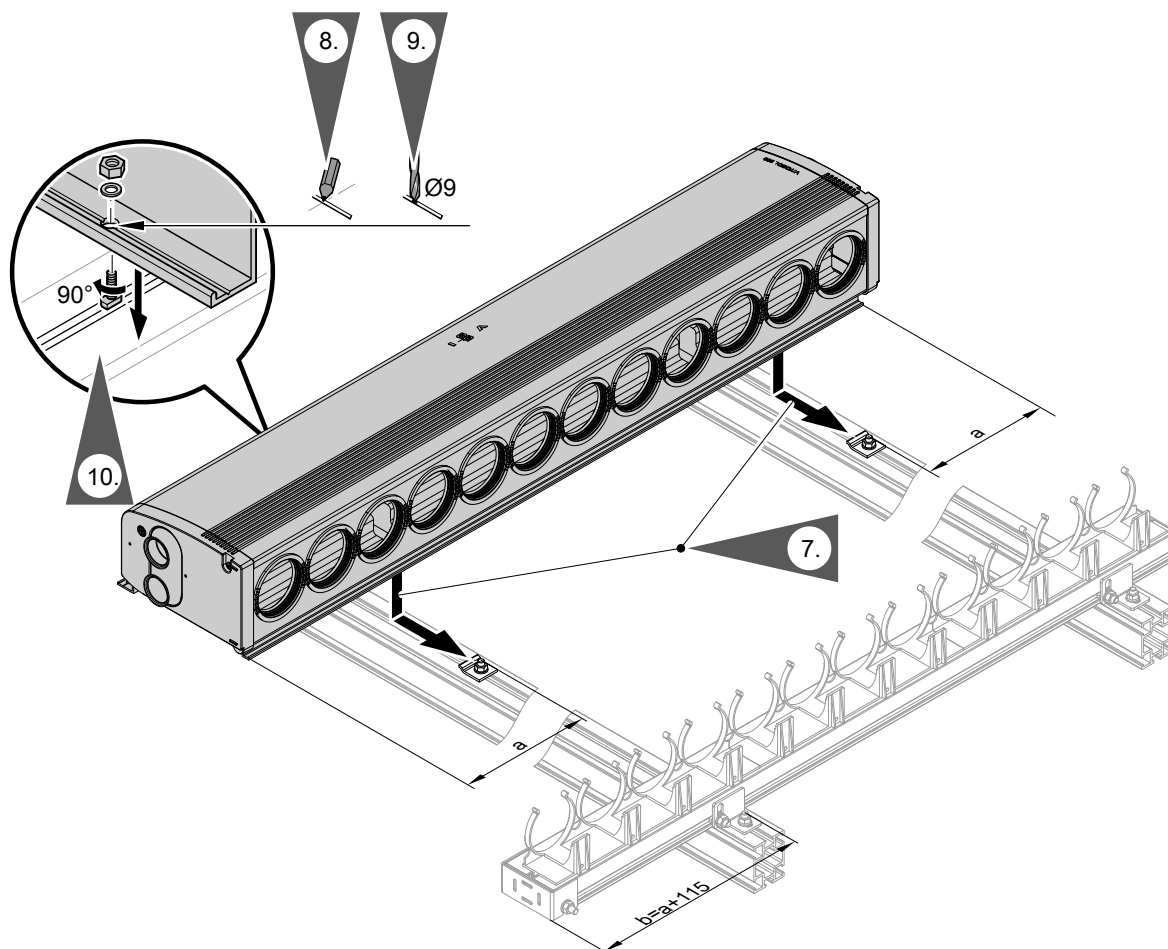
Размер a определяется после расположения соединительного корпуса по центру монтажных шин.
